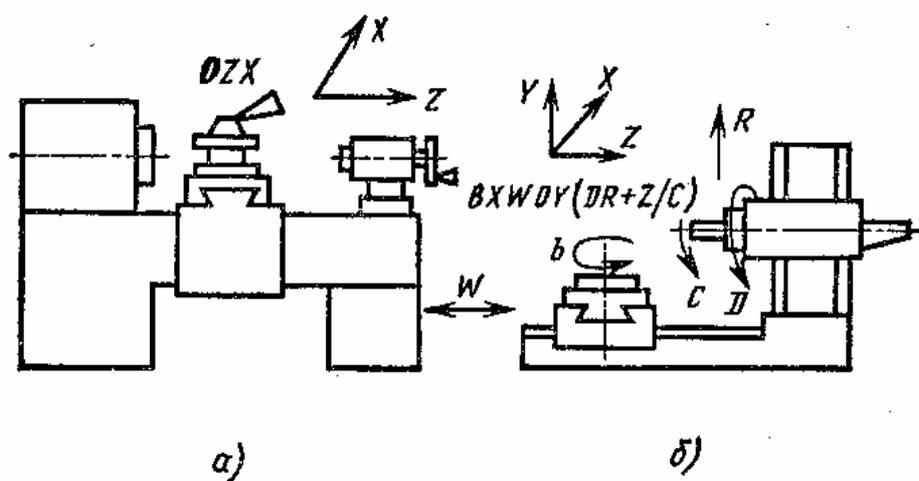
Конструкция и компоновочные схемы токарного и координатно-расточного станков
